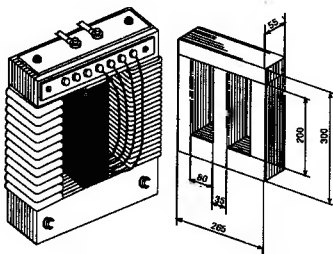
Общий вид сварочного аппарата и его сердечник
